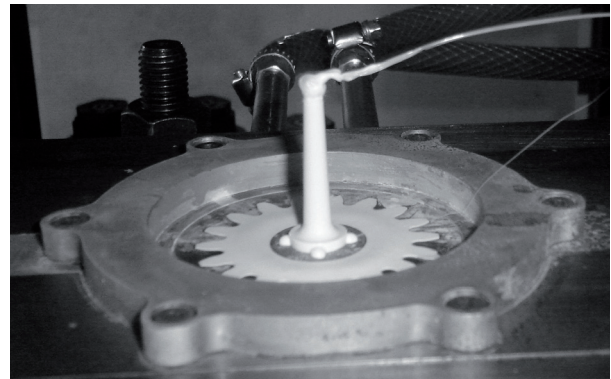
Engrane y colada antes del desprendimiento del molde.
